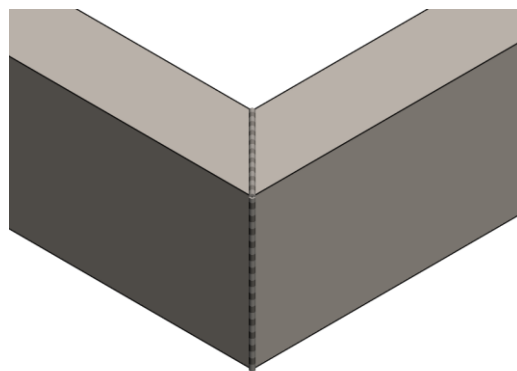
Perfiles tubulares rectangulares soldado
